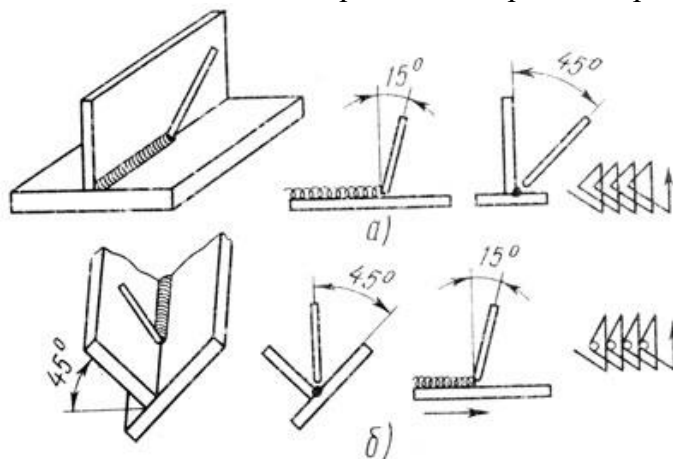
Положение и движения электрода при сварке угловых швов: а - наклонным электродом, б - "в лодочку"
